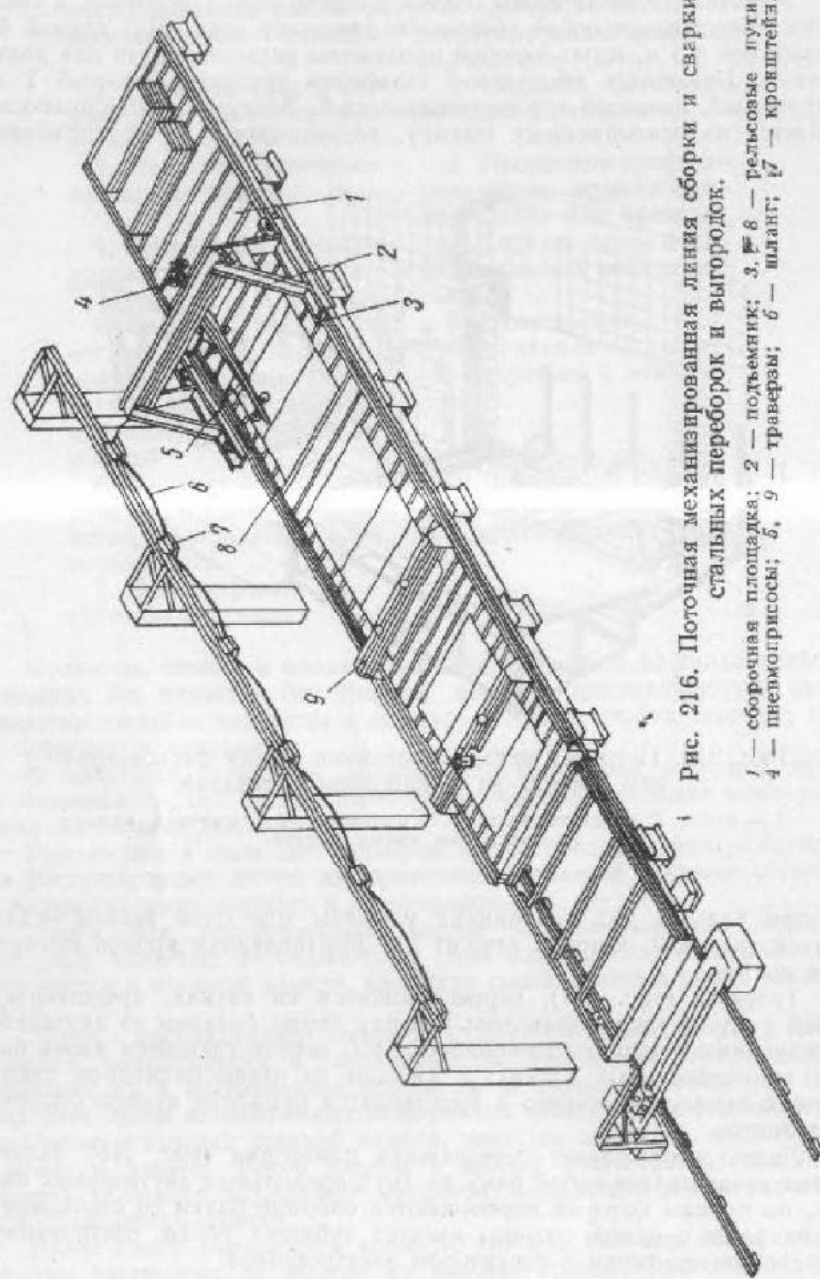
Поточная механизированная линия сборки и сварки стальных переборок и выгородок.
